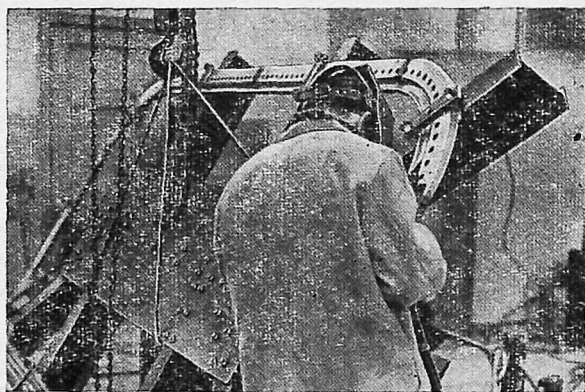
Сварка секционного фланца с поворотом стапеля в удобное положение.
